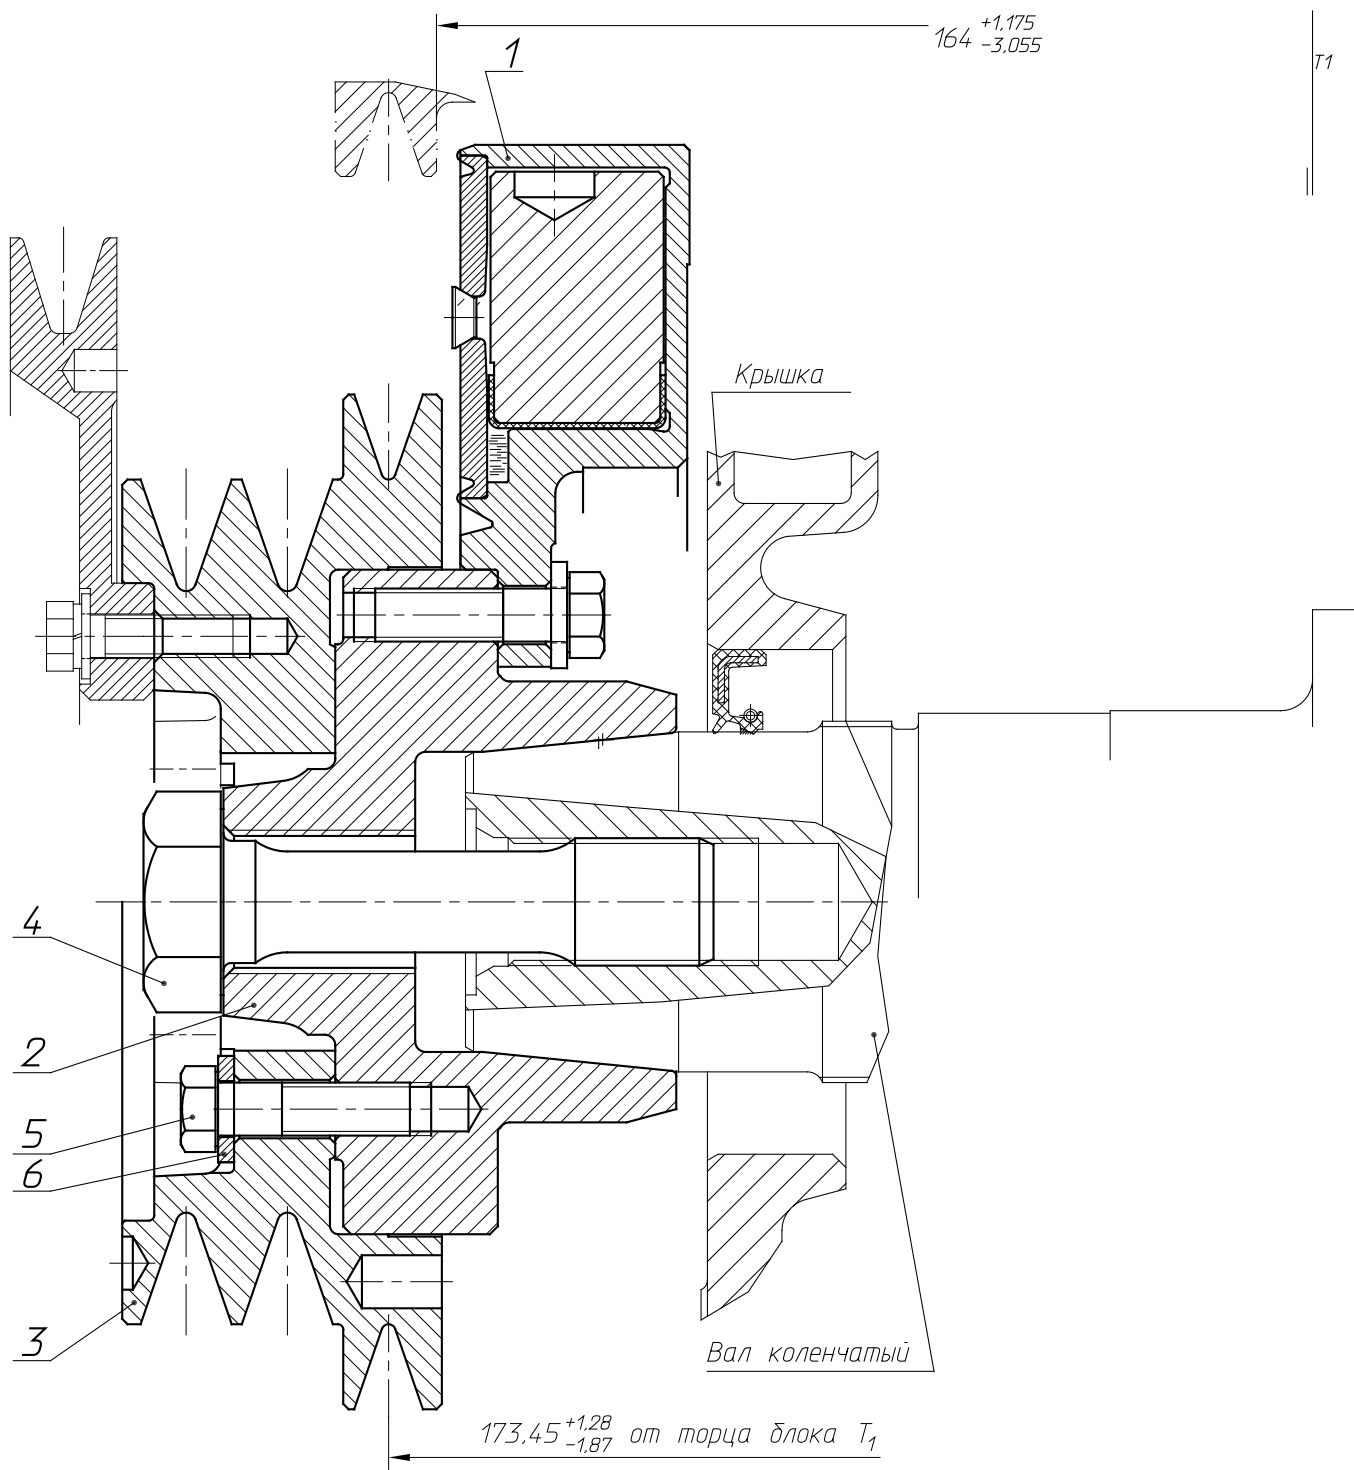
Установка гасителя и шкива на двигатель, 7511.1005050
